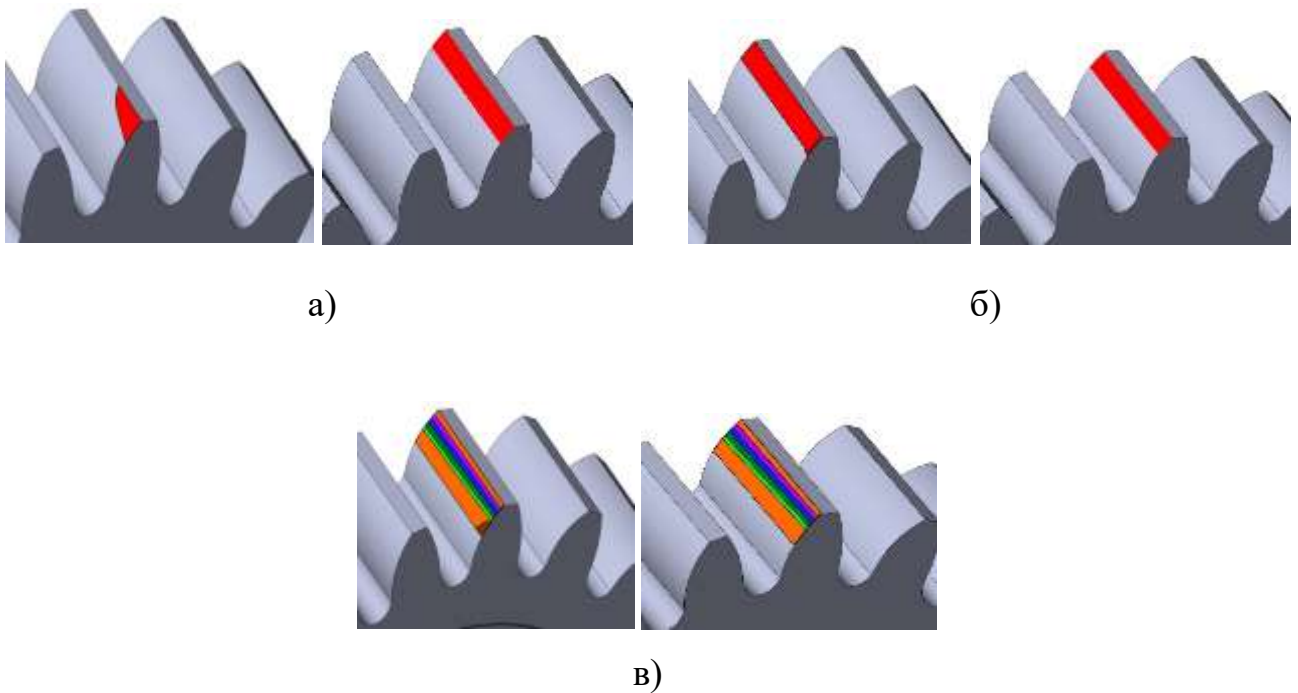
Модель процесу утворення шорсткості поверхні зуба під час фрезерування асиметричного зубчастого колеса
